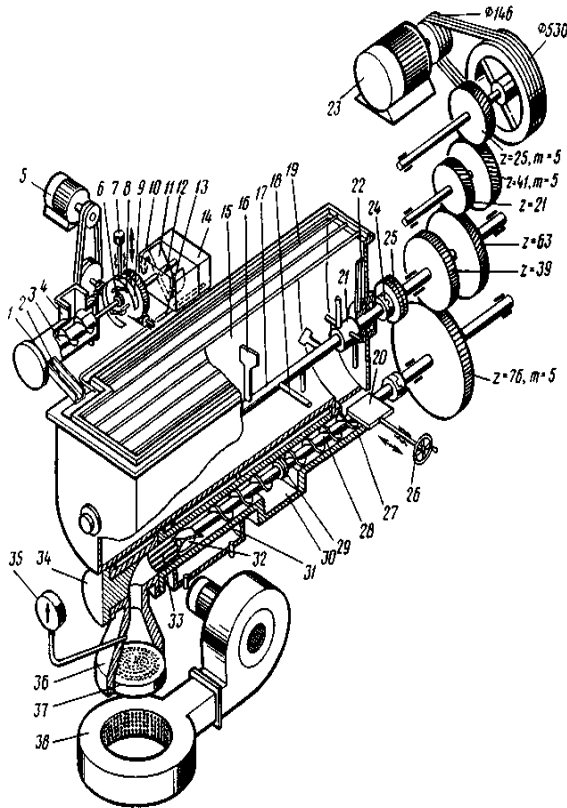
Пресс ЛПЛ-2М: 1 – корпус дозатора; 2 – лоток; 3, 28 – шнеки; 4 – патрубок; 5 – електродвигун; 6 – храпове колесо; 7 – рукоятка; 8 – двоплечий важіль; 9 – півкільце; 10, 14 – бачки; 11 – кишень крильчатки; 12, 17 – вали; 13 – труба; 15 – однокамерна смінь; 16 – лопать; 18 – палець; 19 – кришка; 20 – заслінка; 21 – штовхальник; 22 – ніж; 23 – електродвигун; 24 – муфта; 25 – зірочки; 26 – маховичок; 27 – корпус, що пресує; 29 – шайба; 30 – пропускний канал; 31 – водяна сорочка; 32 – тризахідна ланка; 33 – канавки; 34 – фланець; 35 – манометр; 36 – пресувальна голівка; 37 – матриця; 38 – обдувальний пристрій
